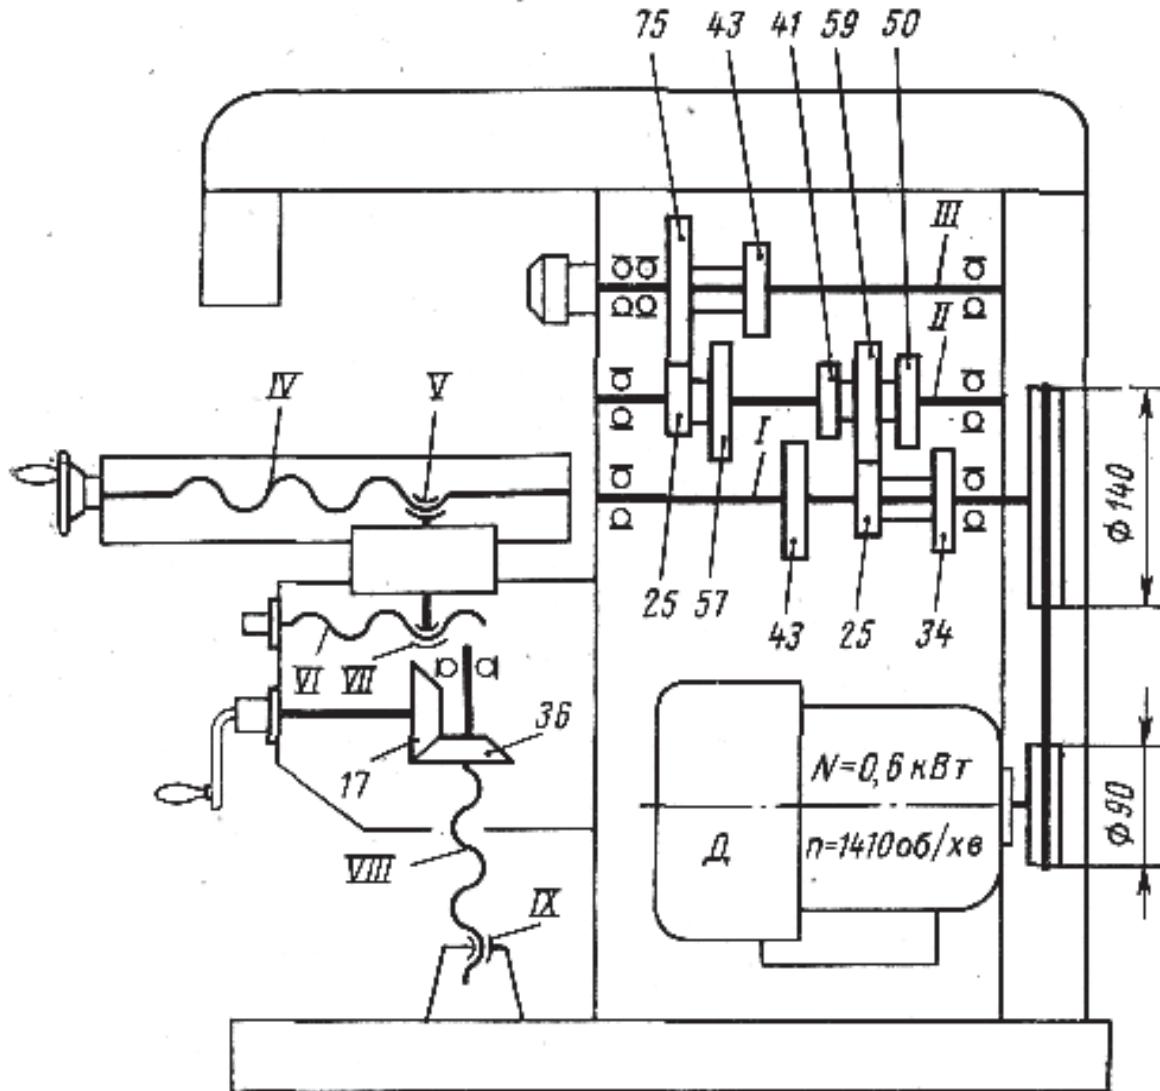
Кінематична схема настільного горизонтально-фрезерного верстата моделі НГФ-110ШЧ
